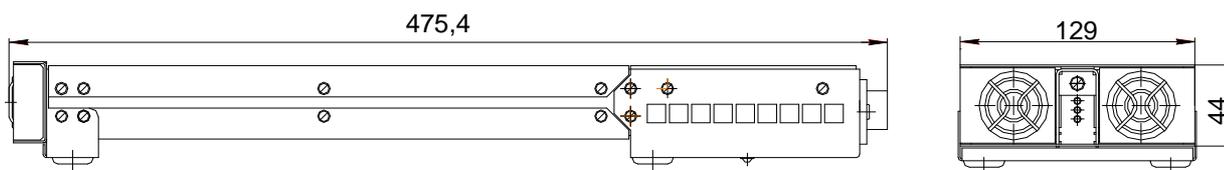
Габаритный чертеж ИЦ-700БП-19
